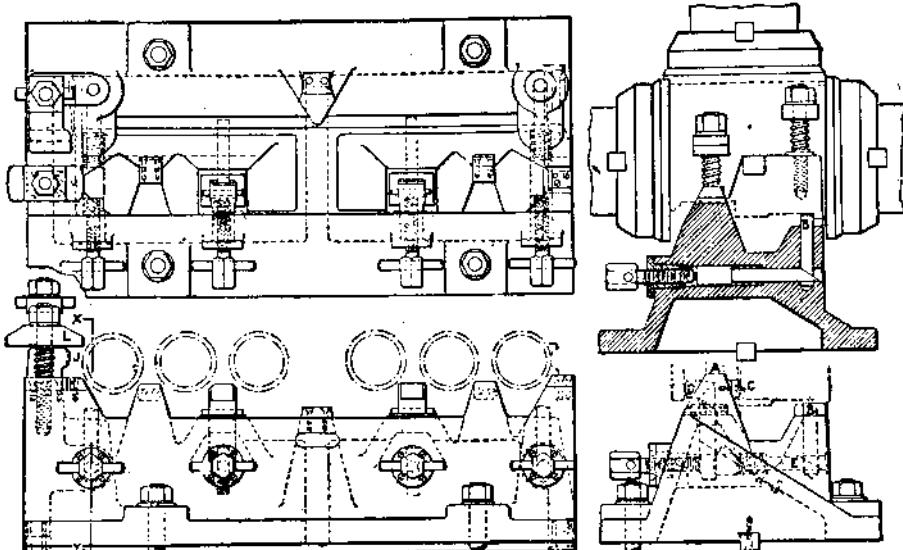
Приспособление для установки блока Cleveland при фрезеровании.
